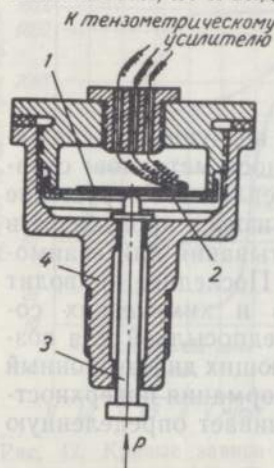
Приспособление для замера силы трения: 1 — тензометрический датчик; 2 — плоская пружина; 3 — шток; 4 — корпус.
